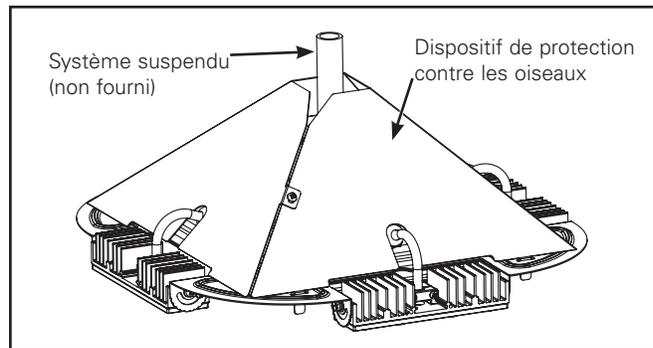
Dispositif de protection contre les oiseaux suspendu (QDPBG)
